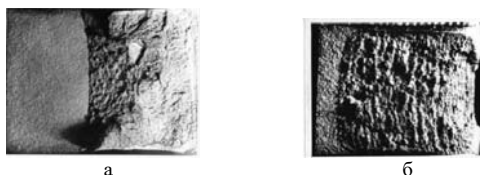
Линии остановки фронта трещины на поверхности излома образцов типа ВР толщиной 50мм, изготовленных из стали 12Х2МФА: а- образец без боковых канавок, б- образец с боковыми канавками
